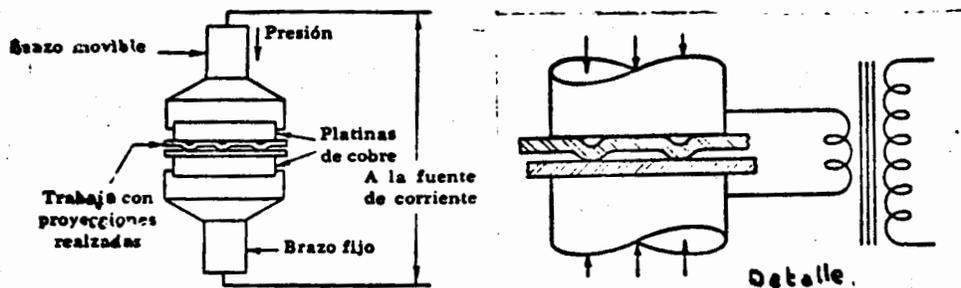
SOLDADURA POR PROYECCION.
